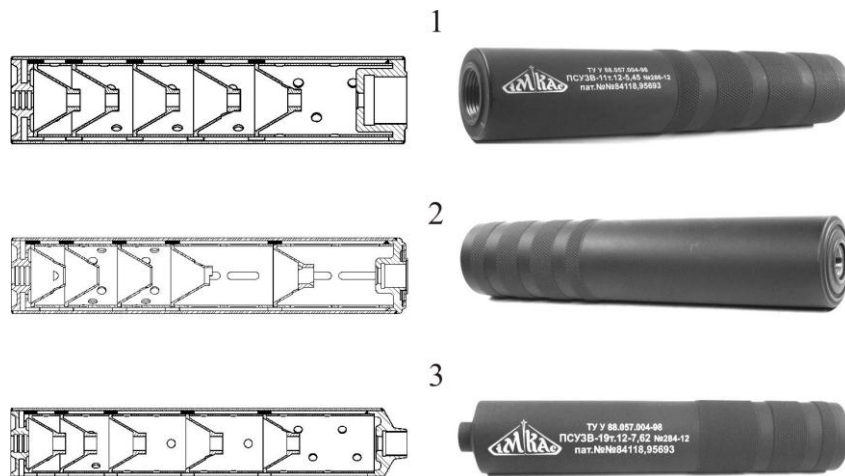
Конструктивная схема и внешний вид приборов снижения уровня звука выстрела: 1 – PCSUZB-11T.12-5,45; 2 – PCSUZB-12TP.12-7,62; 3 – PCSUZB-19TB.12-7,62
